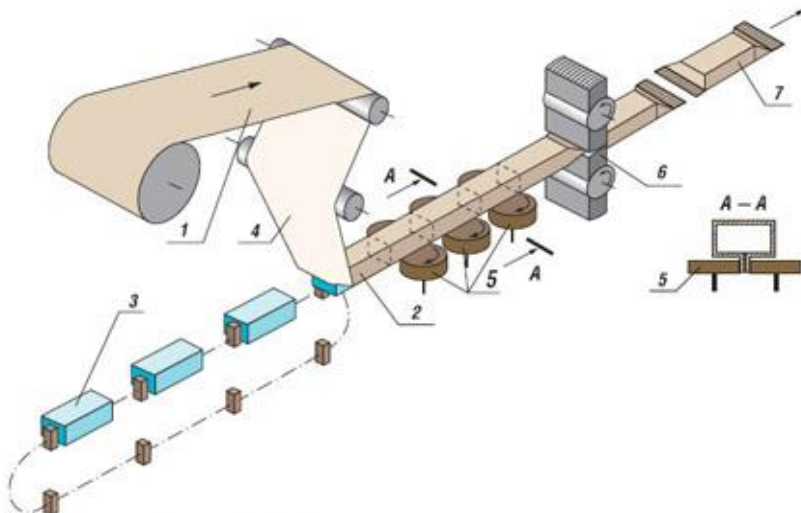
Схема неперервного технологічного процесу пакування штучних виробів в упаковку типу “флоу-пак”: 1 – пакувальний матеріал; 2 – рукав; 3 – виріб; 4 – направляючі валки; 5 – зварні ротори; 6 – ротори зварювання і відрізання; 7 – готова продукція.
